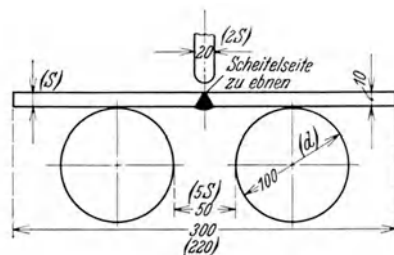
a) Vorrichtung zur Durchführung eines Schweißbiegeversuches nach den Richtlinien. b) Eingeklammert die Abmessungen, wie sie für die D.R.G. vorgeschrieben sind, dann soll  $d = 50$  mm für Blechdicke bis 12 mm,  $d = 100$  mm für Blechdicke über 12 mm sein.
